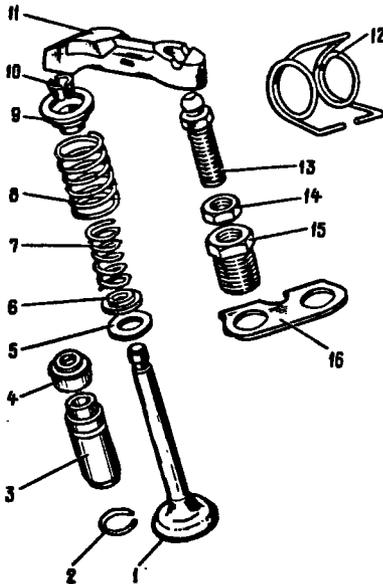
Детали клапанного механизма: 1 - клапан; 2 - стопорное кольцо; 3 - направляющая втулка; 4 - маслоотражательный колпачок; 5 - опорная шайба наружной пружины; 6 - опорная шайба внутренней пружины; 7 - внутренняя пружина; 8 - наружная пружина; 9 - тарелка пружины; 10 - сухари; 11 - рычаг привода клапана; 12 - пружина рычага; 13 - регулировочный болт; 14 - контргайка регулировочного болта; 15 - втулка регулировочного болта; 16 - стопорная пластина пружины рычага
